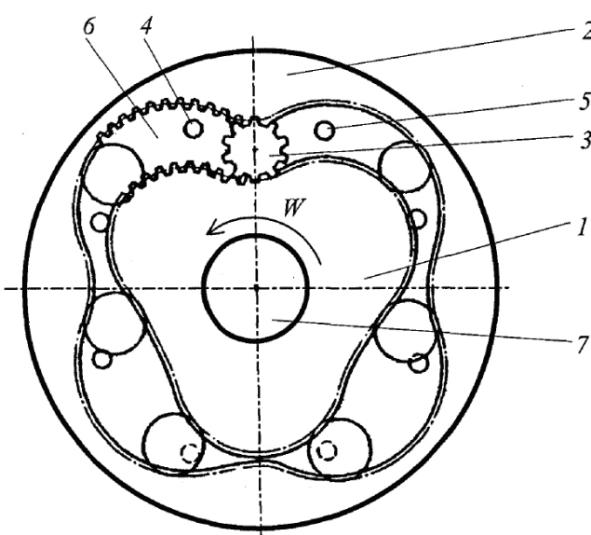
Роторний планетарний гідромотор с плаваючими сателітами: 1 – сонячне колесо с наружними зубьями, 2 – сонячне колесо с внутрішніми зубьями, 3 – сателіт, 4 – підводячий канал робочої жижки, 5 – канал для відвода робочої жижки, 6 – робоча камера, 7 – вал сонячного колеса с наружними зубьями
